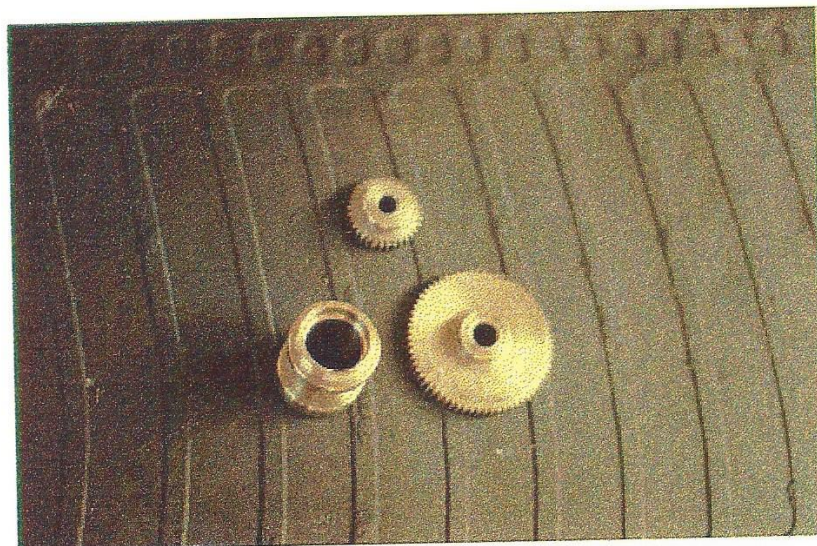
Engrenagem maior (à direita) / engrenagem menor (à esquerda) e o mancal.
